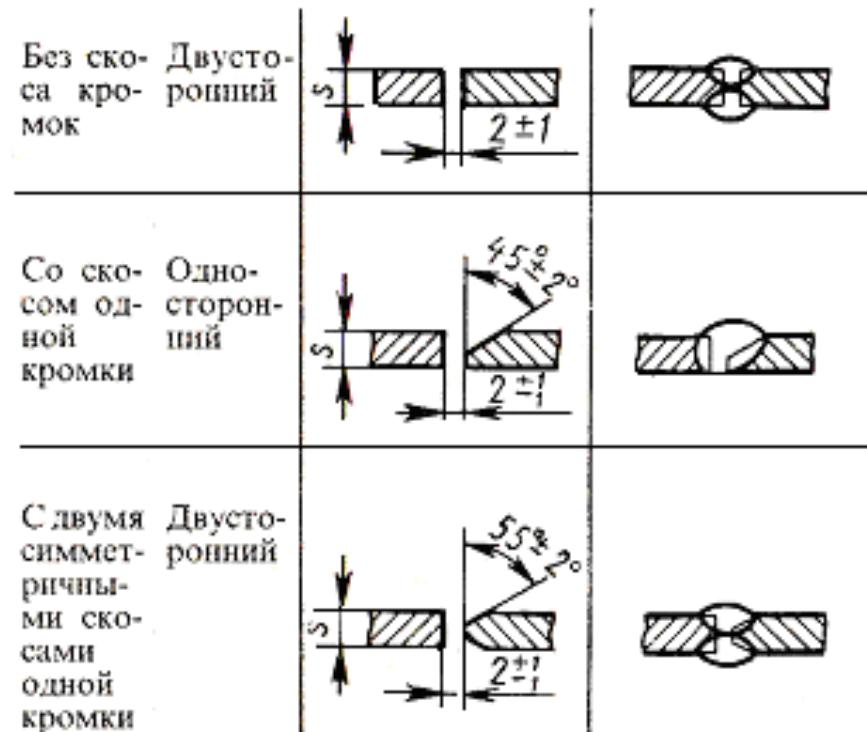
Виды сварных стыковых соединений
